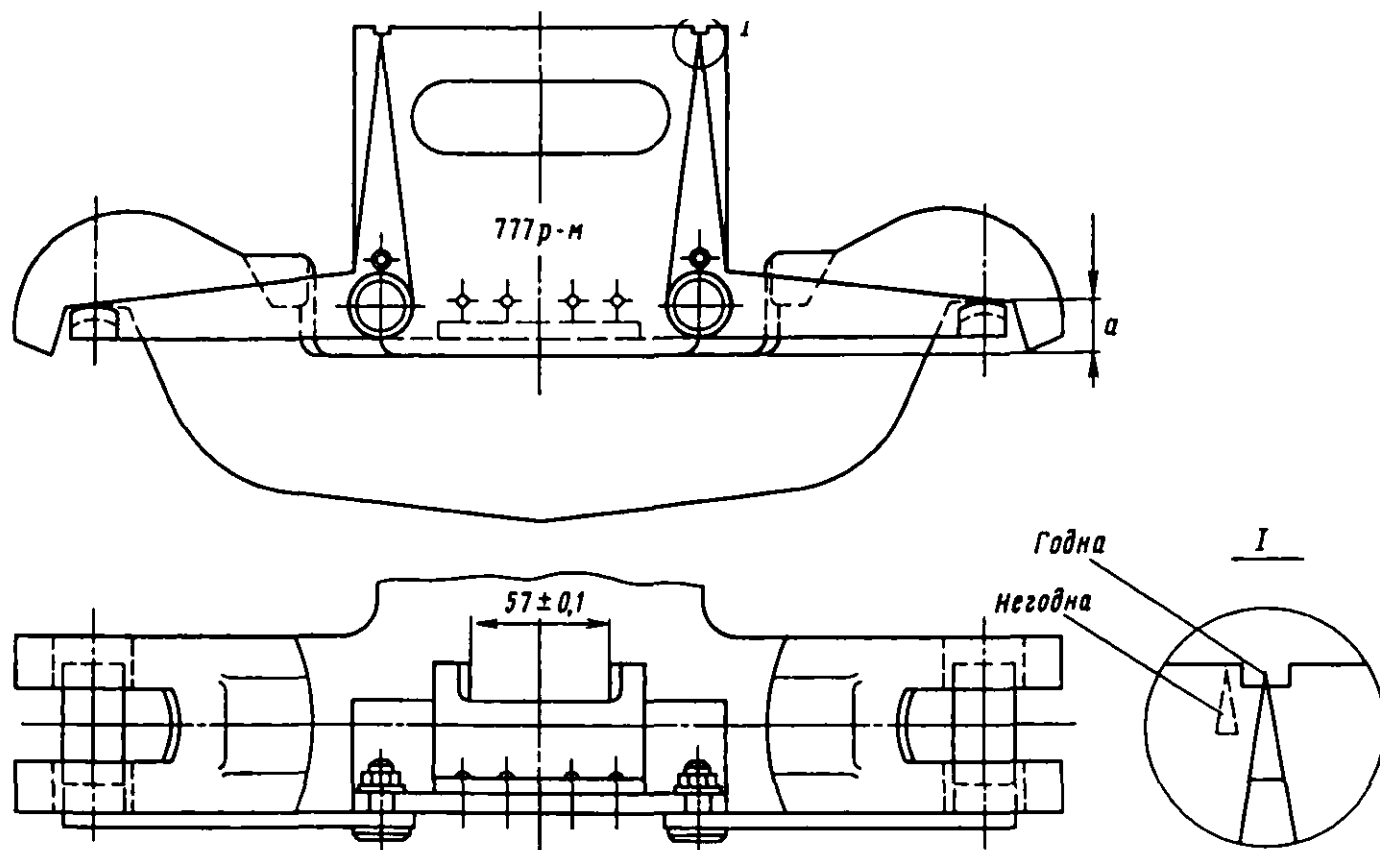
Проверка центрирующей балочки шаблоном 777р-м или 780р-м
